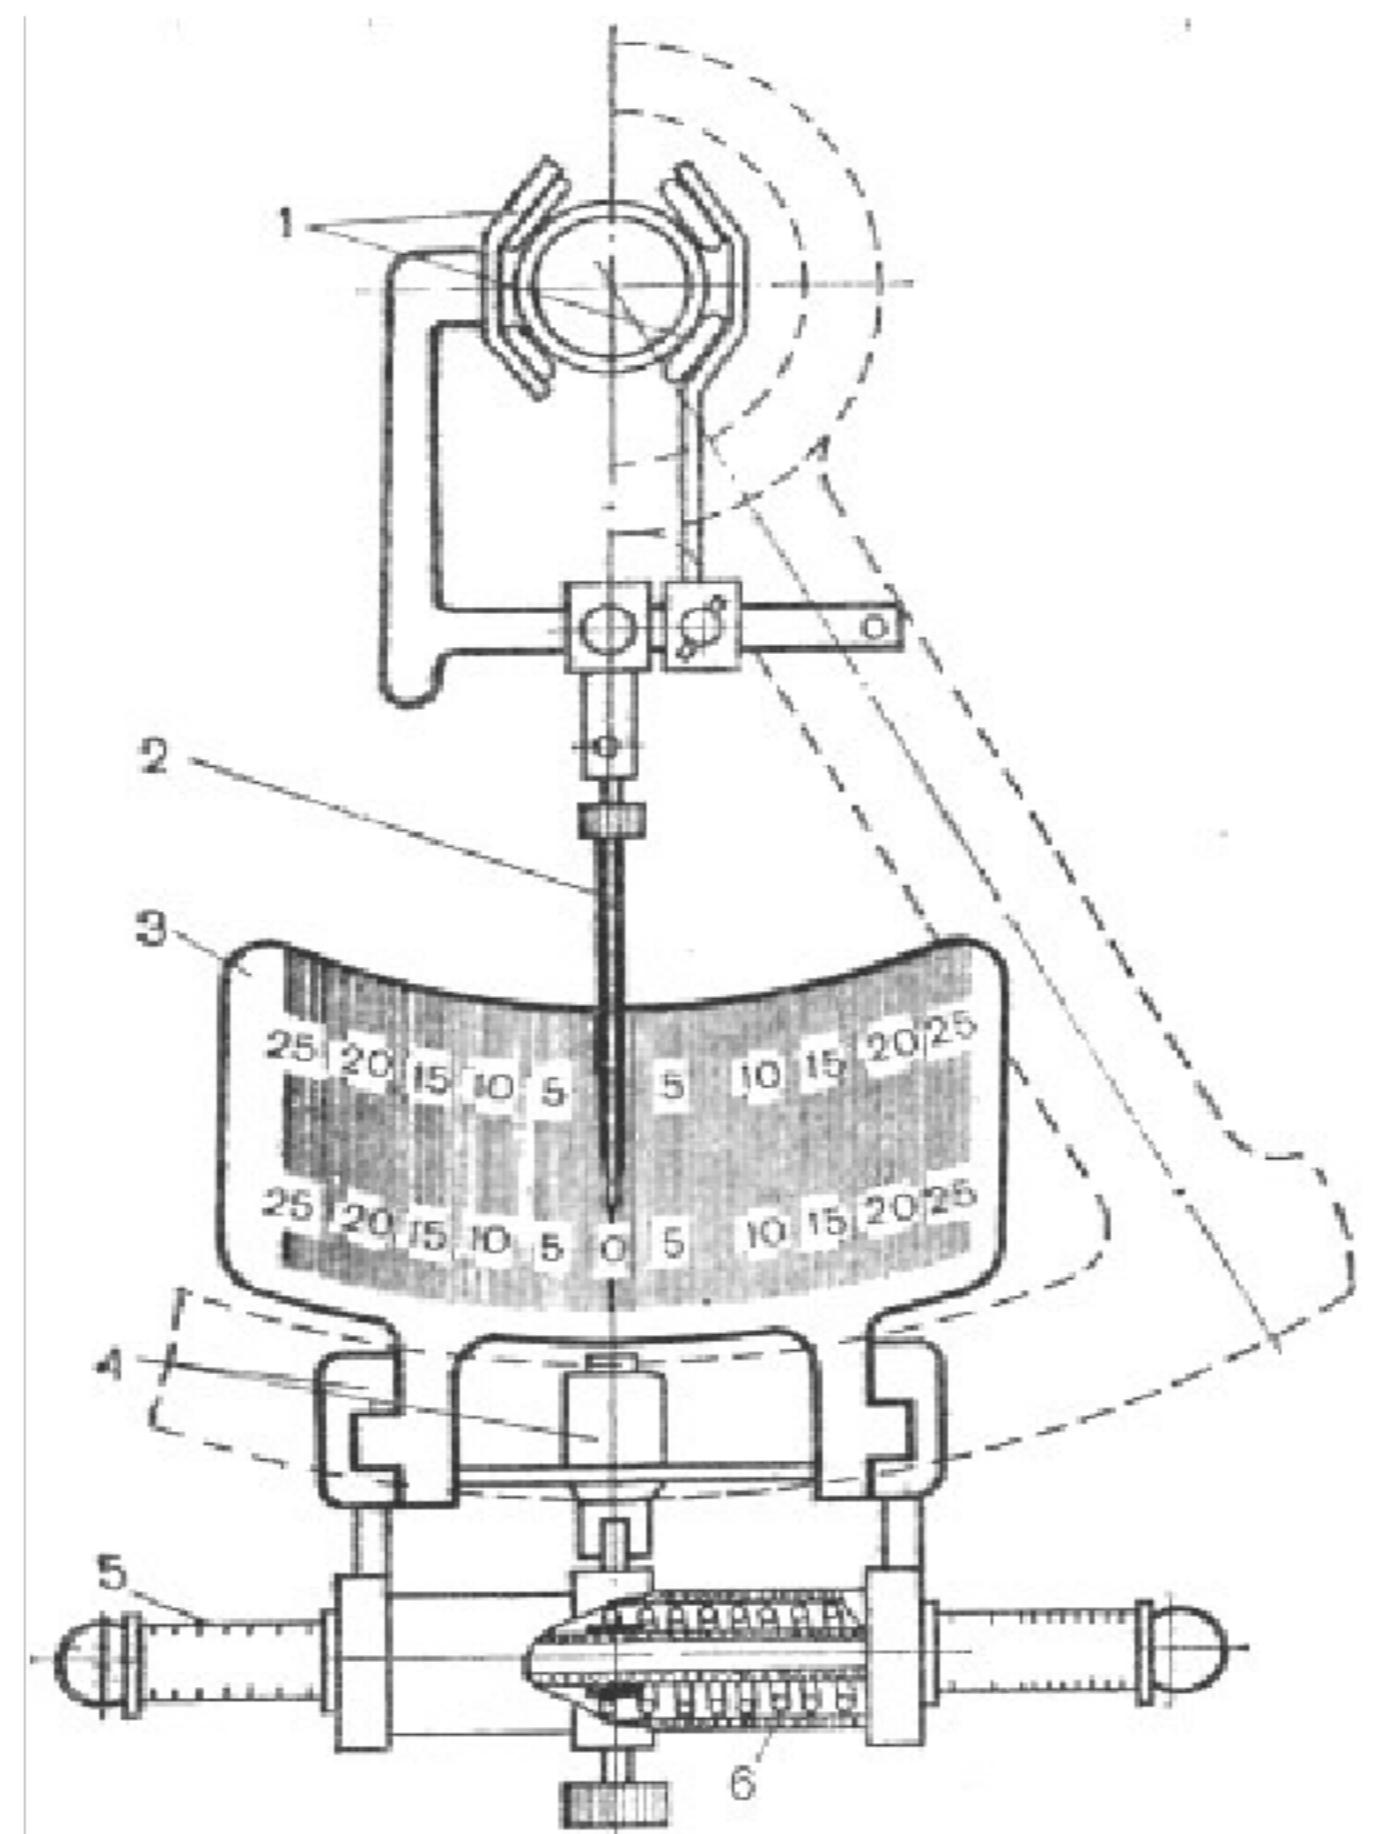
Прибор К-187: 1 – захваты рулевой колонки; 2 – указательная стрелка, закреплённая на валу рулевой колонки; 3 – шкала люфтометра; 4 – зажимы для крепления на рулевом колесе; 5 – динамометрическая рукоятка; 6 – пружина регулировки прибора.
